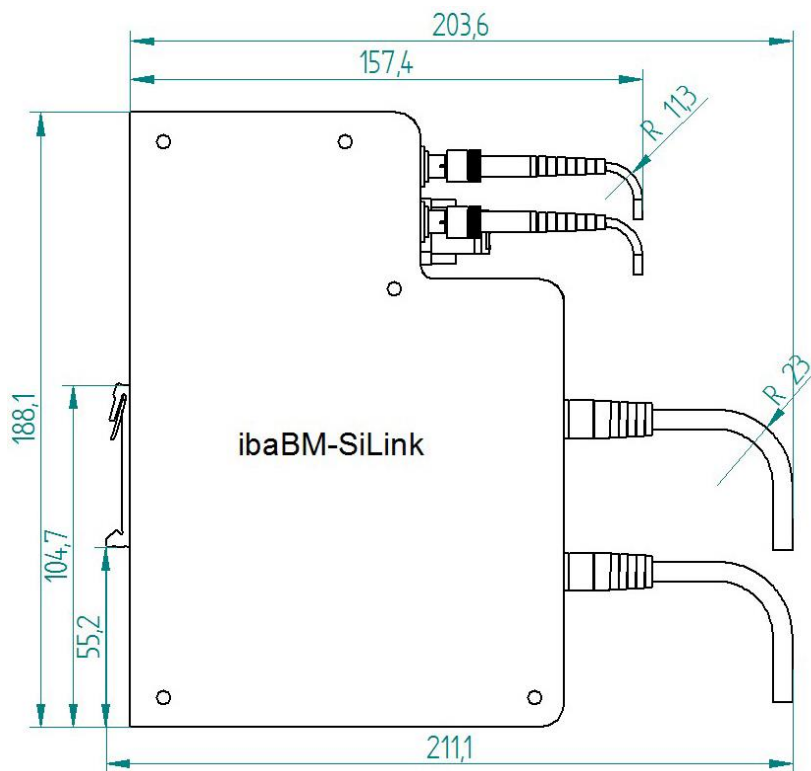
Чертеж с размерами устройства с кабелями (размеры в мм)
